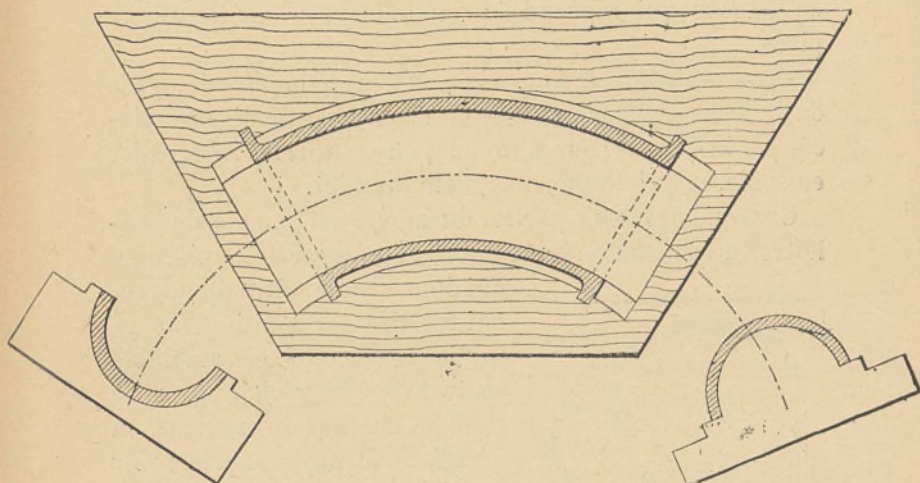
Gabarit et trousses pour troussage d'un coude.
